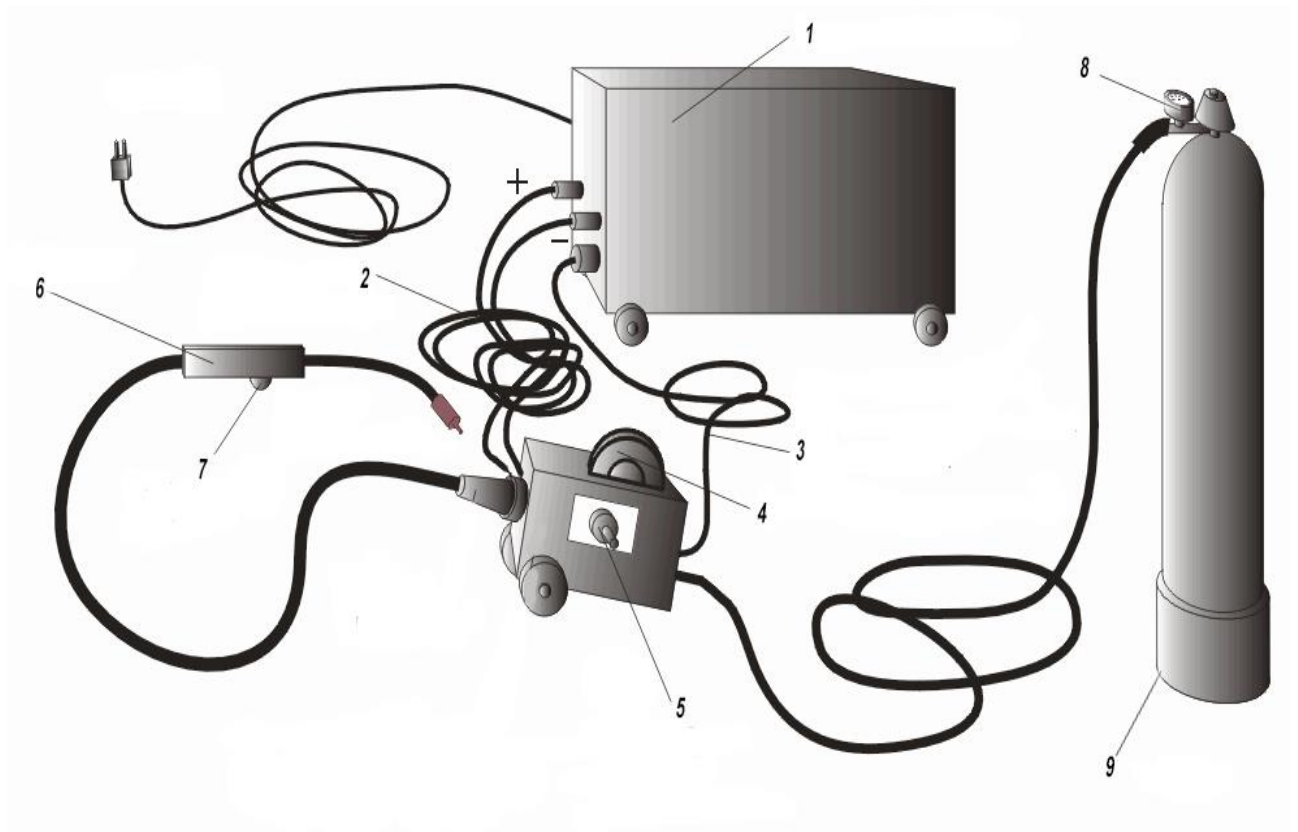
Основне обладнання для напівавтоматичного зварювання
